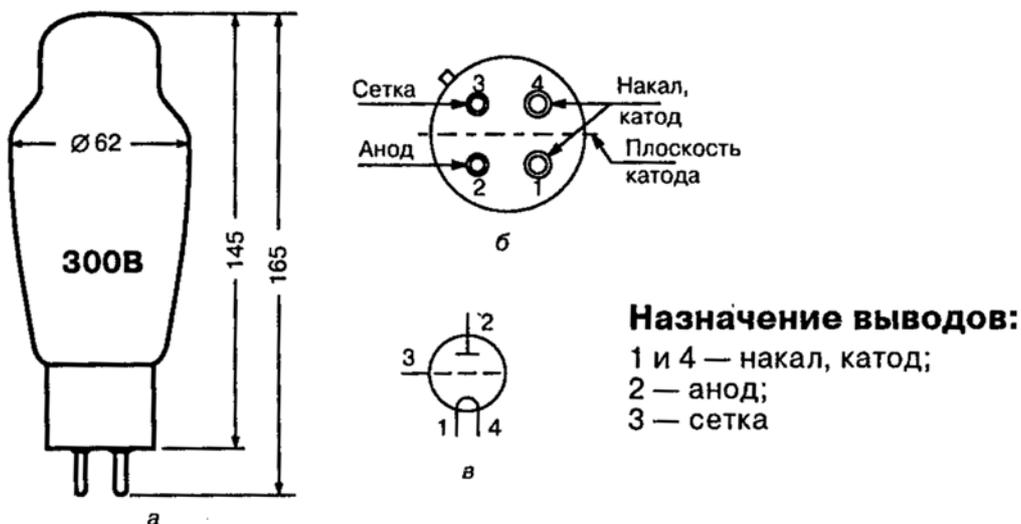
Лампа 300В: а — основные размеры; б — вид со стороны штырьков; в — схематическое изображение
